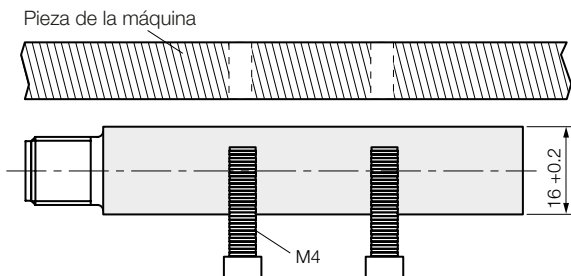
Montaje de la cabeza del sensor (sin cuerpo aislante)
